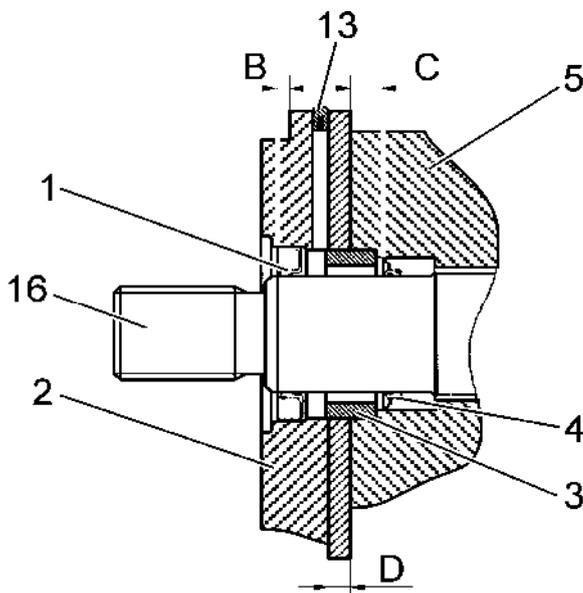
С.33. Установочные размеры уплотнительных колец и монтажного фланца насоса трансмиссии
